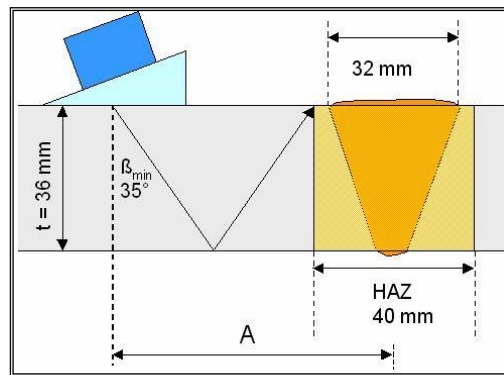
Ángulo de proyección para soldadura a tope ^[13]
